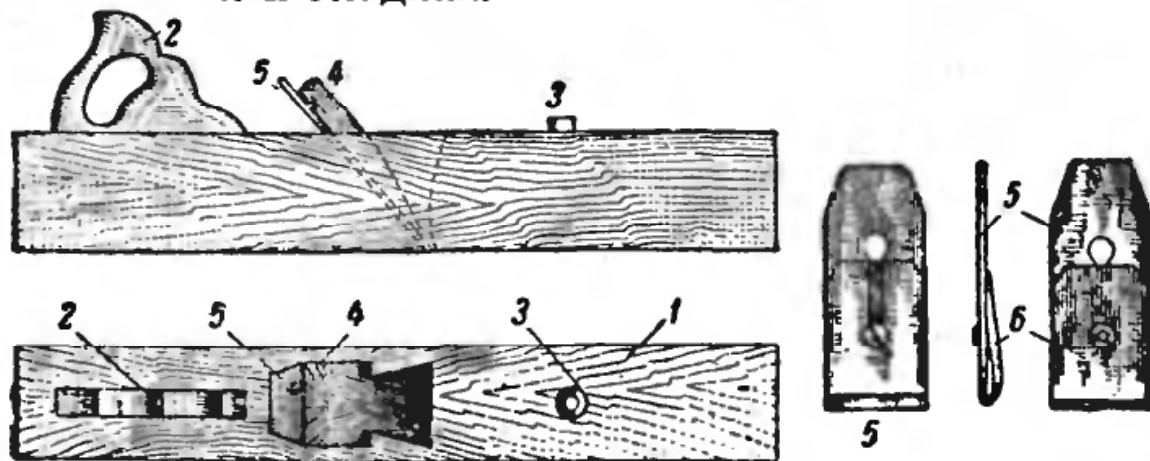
Фуганок: 1 — колодка, длина 600—700 мм; 2 — ручка; 3 — пробка; 4 — клин; 5 — железка, ширина 65—75 мм; 6 — горбати́к.
